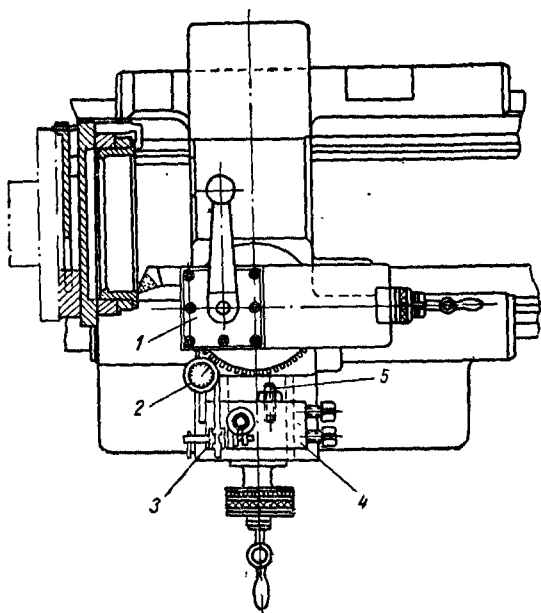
Схема установки с индикаторным устройством для точного растачивания.
